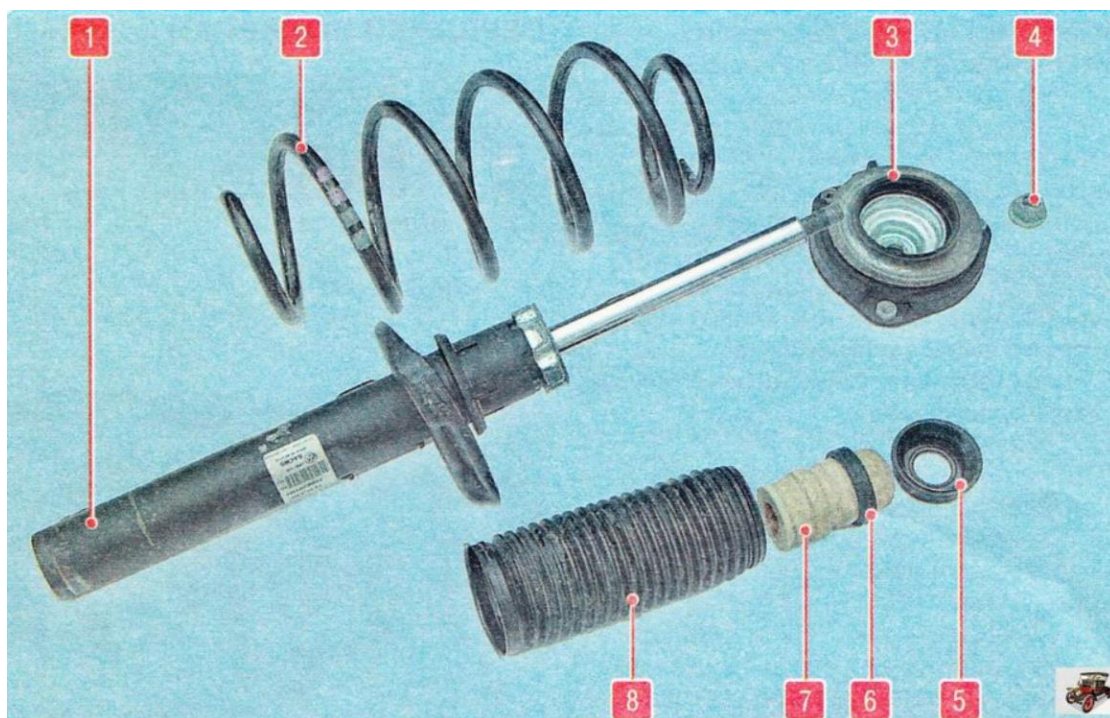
Деталі амортизаційної стійки: 1 – амортизатор; 2 – пружина; 3 – верхня опора; 4 – гайка штока амортизатора; 5 – захисний ковпачок; 6 – стопорне кільце кожуха; 7 – буфер ходу стиснення; 8 – пильник (захисний кожух).
